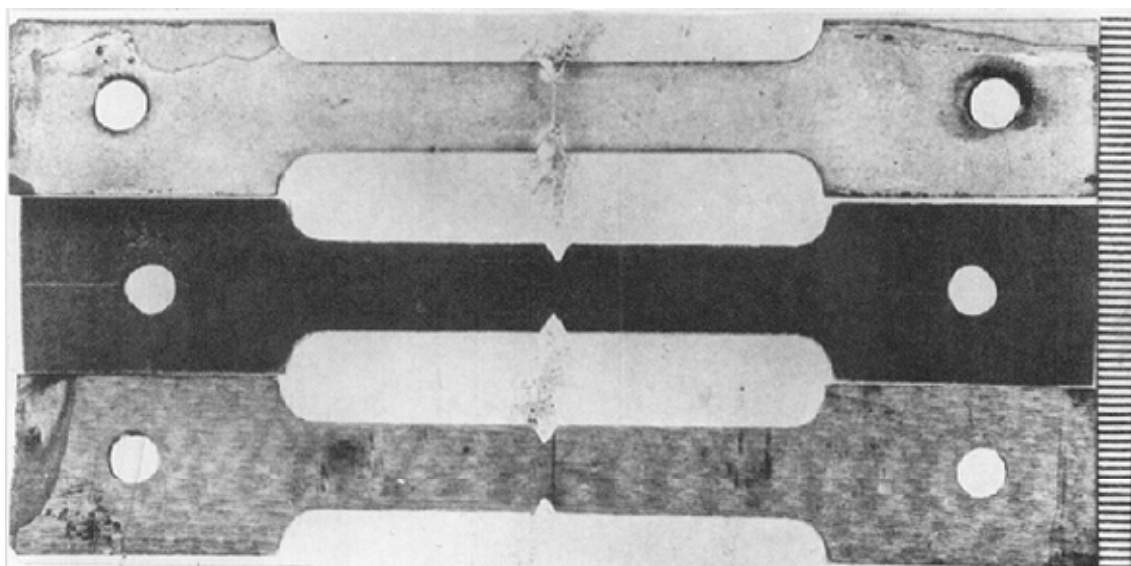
Образцы, изготовленные из заготовок турбинных лопаток
